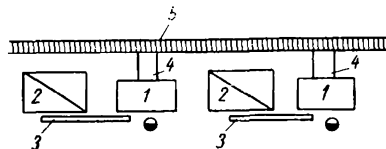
Схема расположения стационарного пластинчатого транспортера в линии легких штамповочных молотов: 1 — штамповочные молоты; 2 — нагревательные печи; 3 и 4 — склизы; 5 — стационарный пластинчатый транспортер
